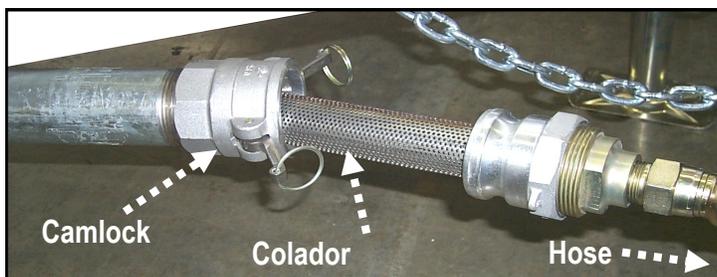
Asamblea de Colador (entre la bomba y la manguera)
